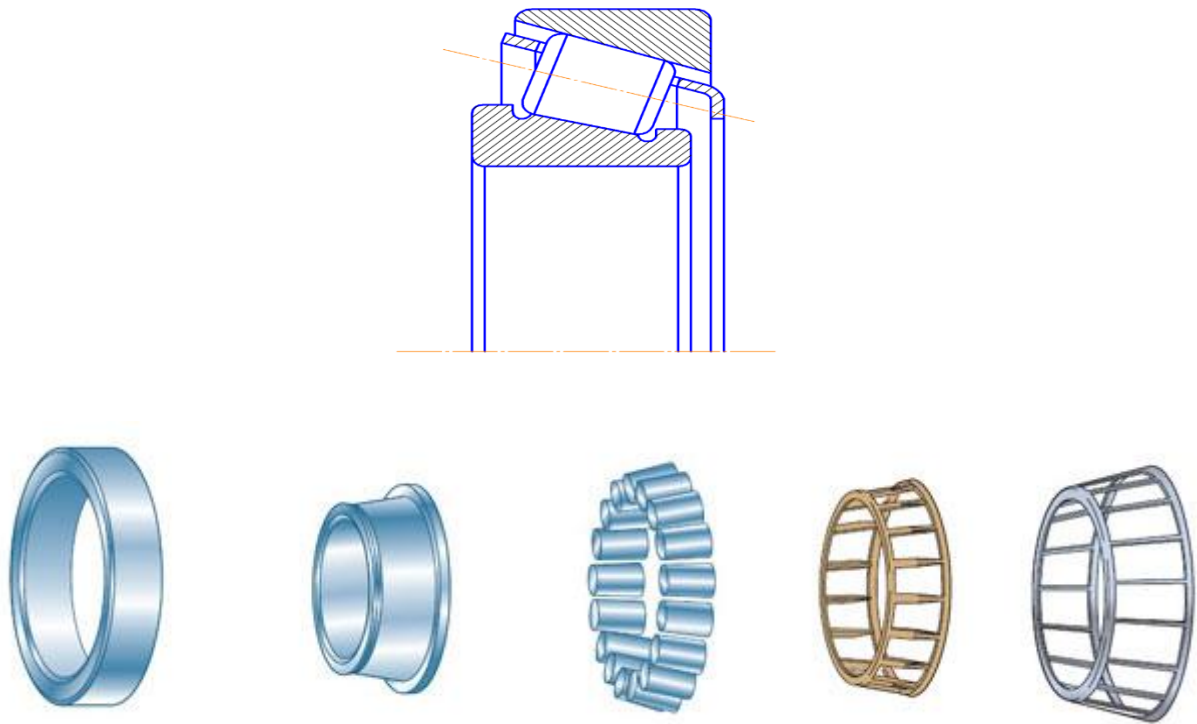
Конструкція роликового радіально-упорного підшипника
